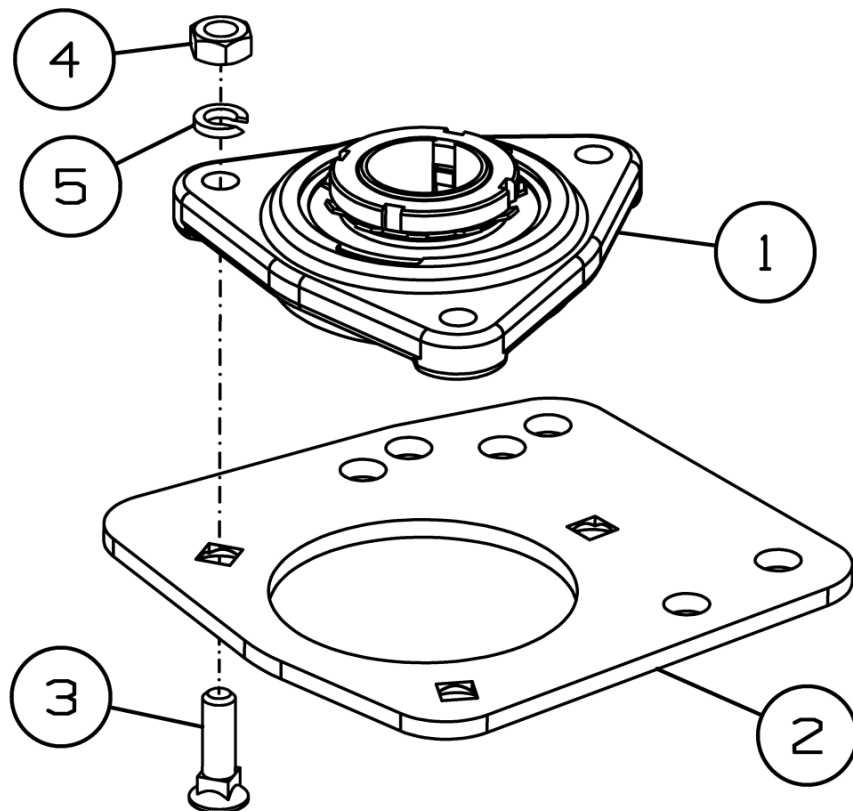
Корпус подшипника SS-780.01.06.140
